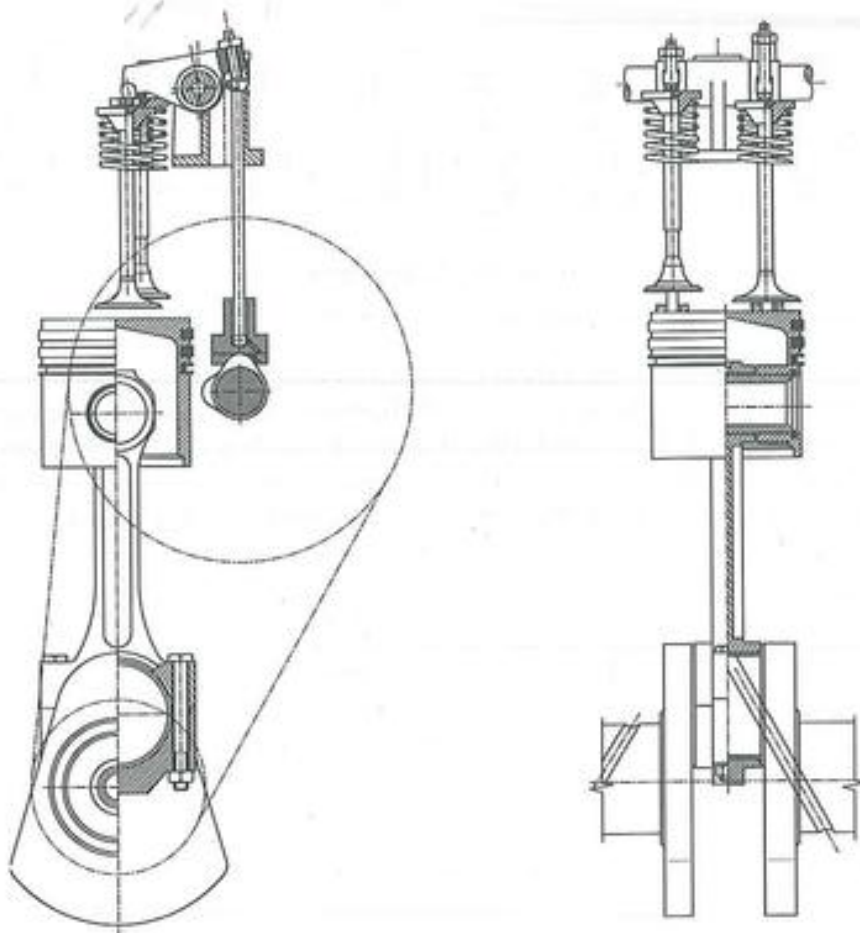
El mecanismo biela-manivela. Motor de explosión.
